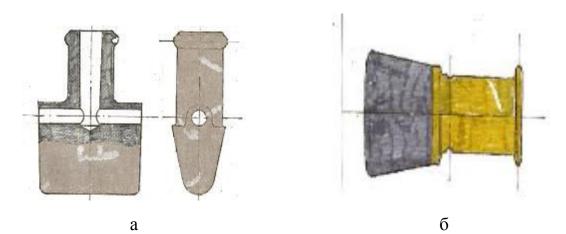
Инструмент формовочный: а - башмак с резиновым наконечником формовочным;
